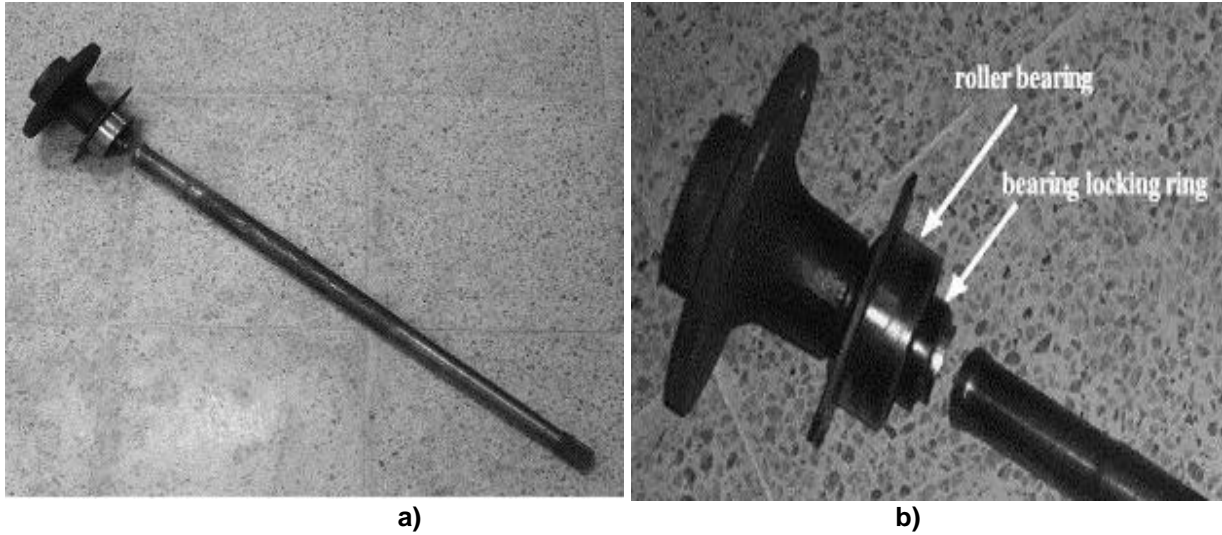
Rotura de eje bajo flexión rotativa donde, a) Vista general del eje defectuoso en la condición de recepción, b) Primer plano de la localización de la fractura [12].
